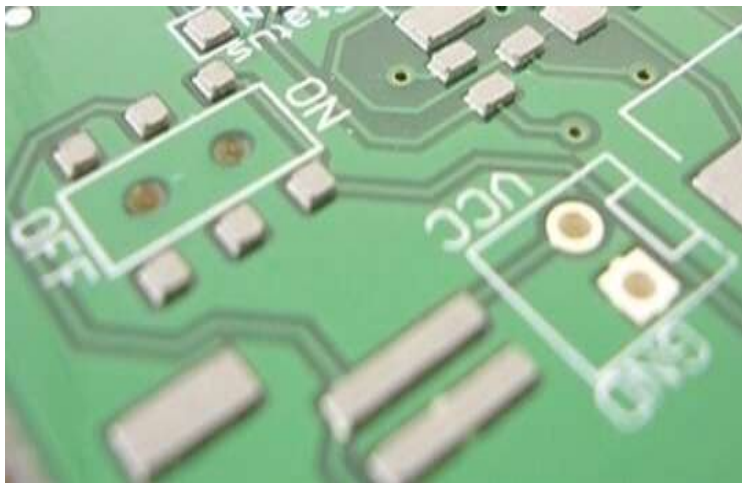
Soldadura en pasta sobre pcb [18].
